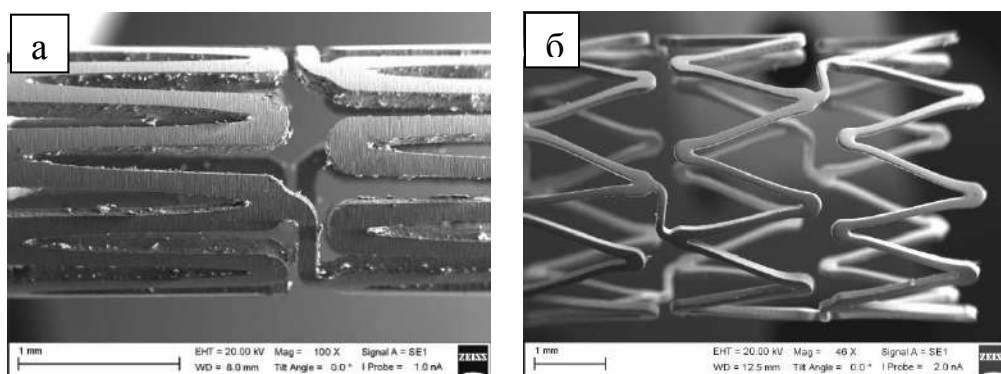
Заготовка стента после лазерной вырезки из трубки (а), дизайн стентов (б)
